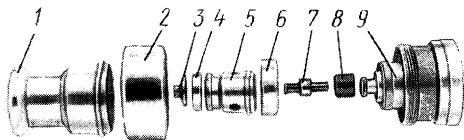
Унифицированные детали катодного узла сварочных пушек:
